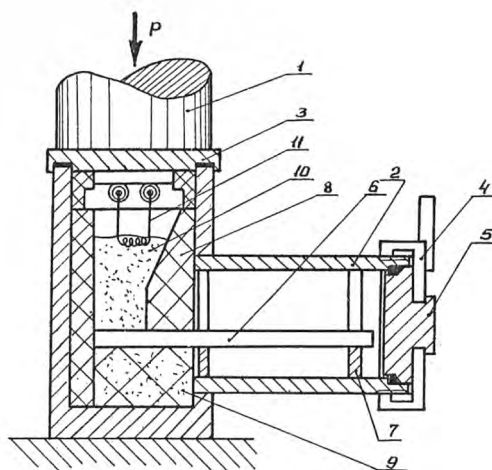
Универсальный пресс-реактор: 1 — шток пресса; 2 — корпус; 3 — крышка вертикальной камеры; 4 — затвор лепестковый; 5 — грибок горизонтальный; 6 — наплавляемая деталь с реакционной шихтой (10); 7 — опоры; 8 — графитовая футеровка; 9 — теплоизоляция; 11 — инициирующее устройство
